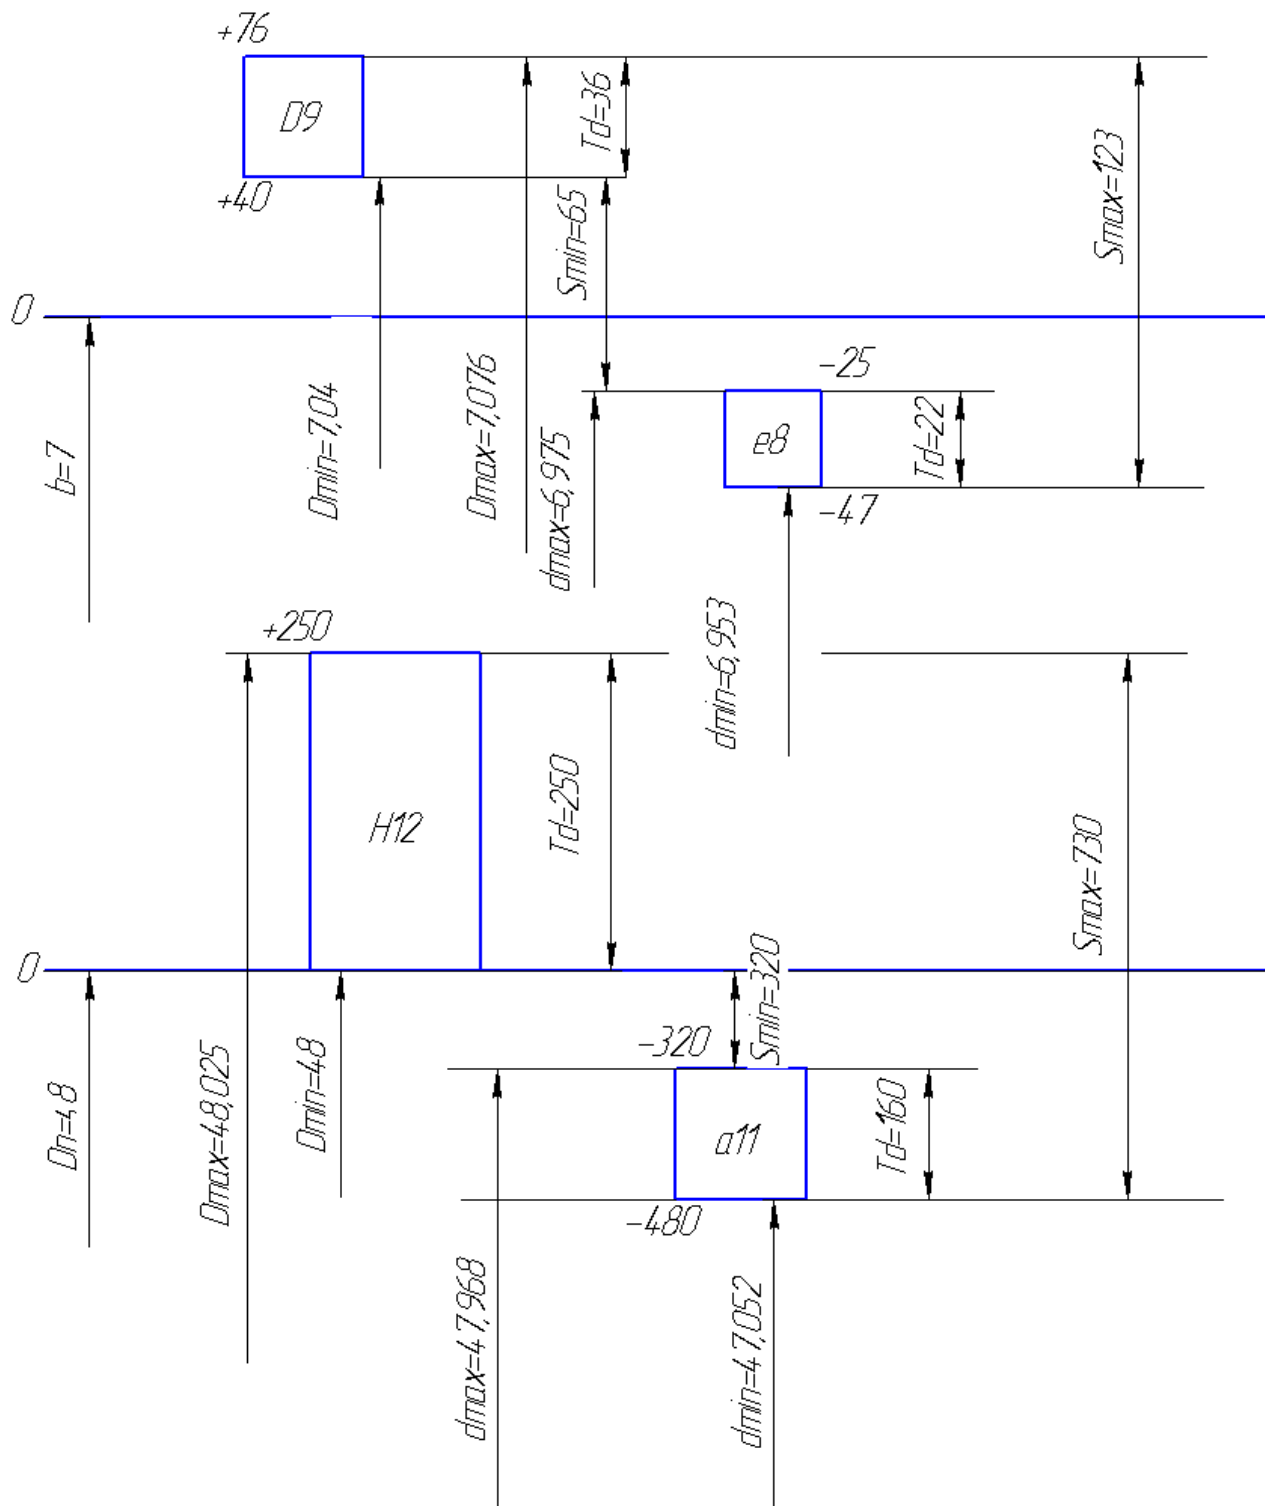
Схемы расположения полей допусков деталей шлицевого сопряжения.
